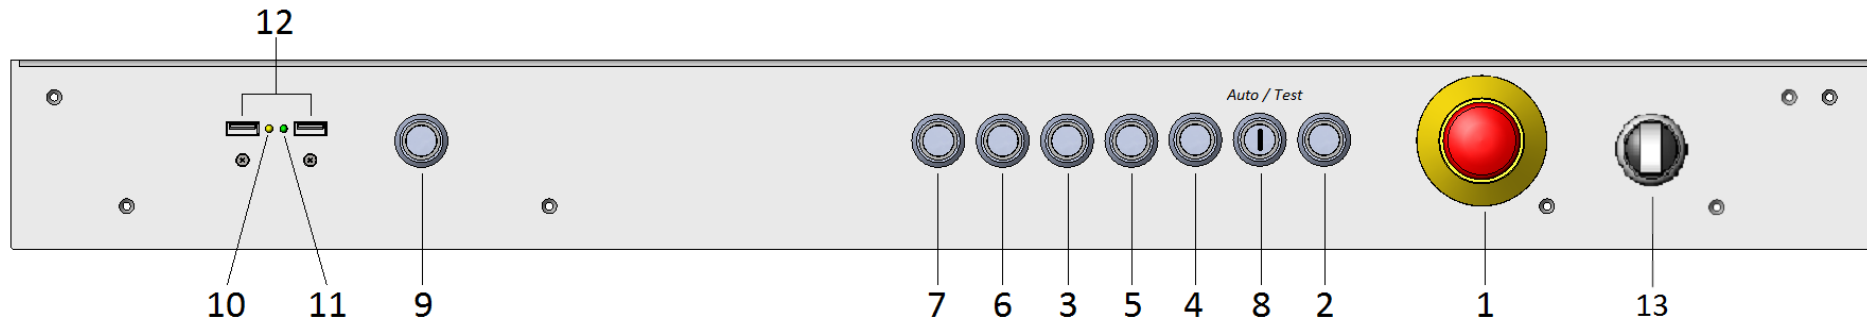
Detail: Maschinenbedienelemente Standardmaschine
